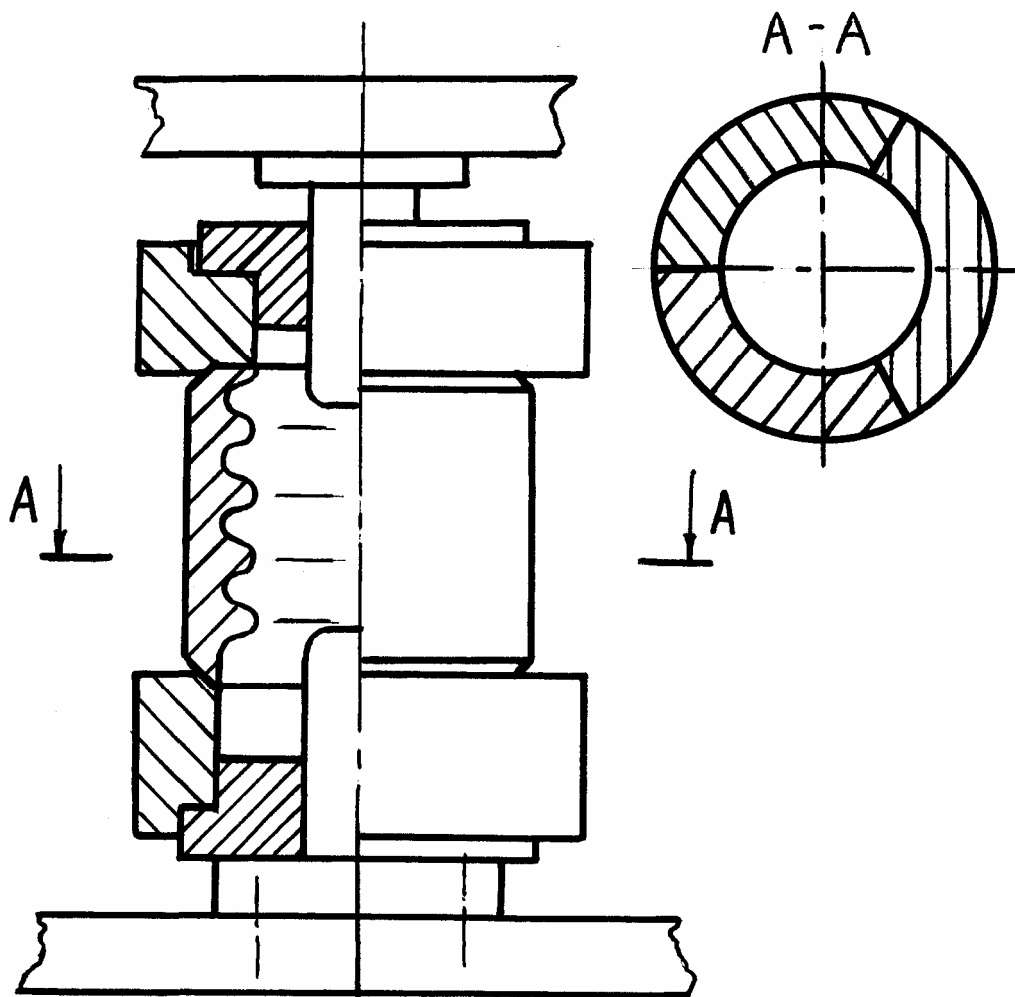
Конструктивна схема прес-форми для формоутворення заготовок виробу типу "опорний ізолятор"
